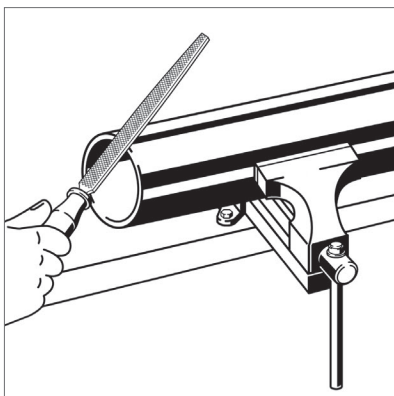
Rohr innen und außen fachgerecht entgraten.
